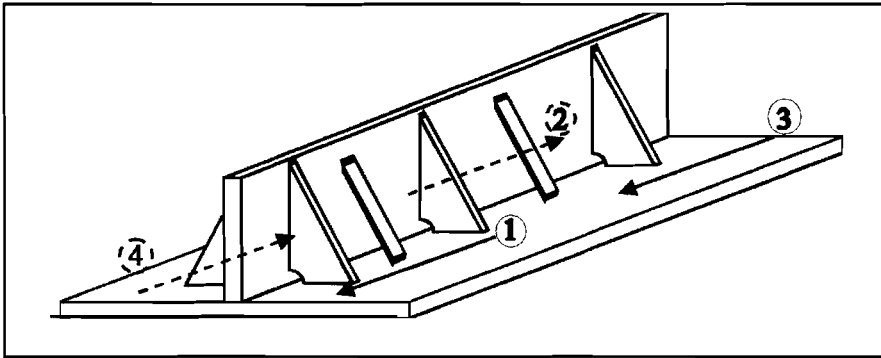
SECUENCIA PARA SOLDAR UNIONES EN ÁNGULO
